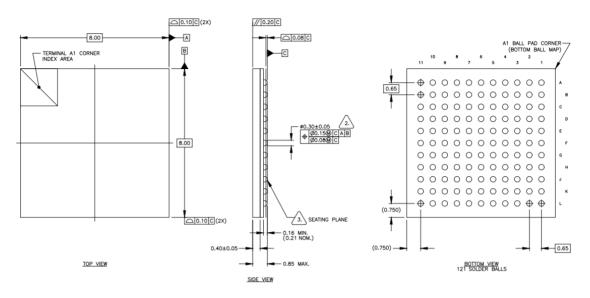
MH1903 BGA1218mm×8mm 封装尺寸
